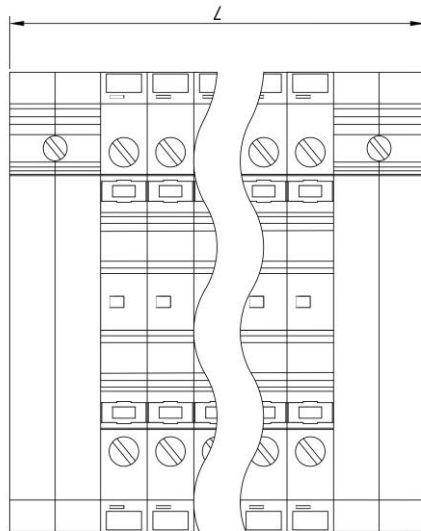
Общий вид базового блока ЭПББ. Вид сзади.
